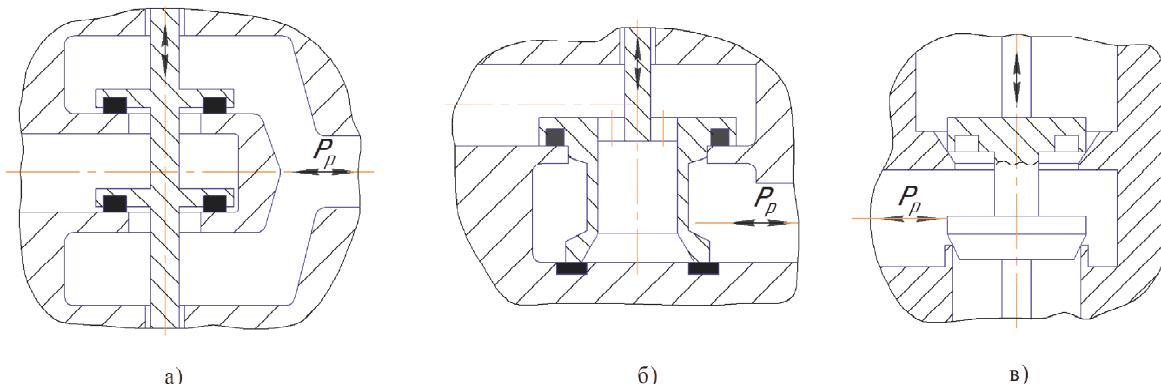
Конструктивные реализации двухседельного способа разгрузки: а, г – золотникового типа; б – трубчатого типа.
